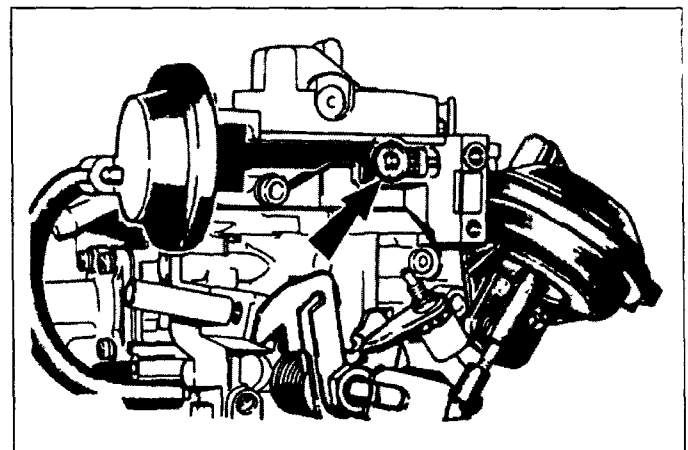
б. Фиксатор (указан стрелкой) крепления рычага диафрагмы
